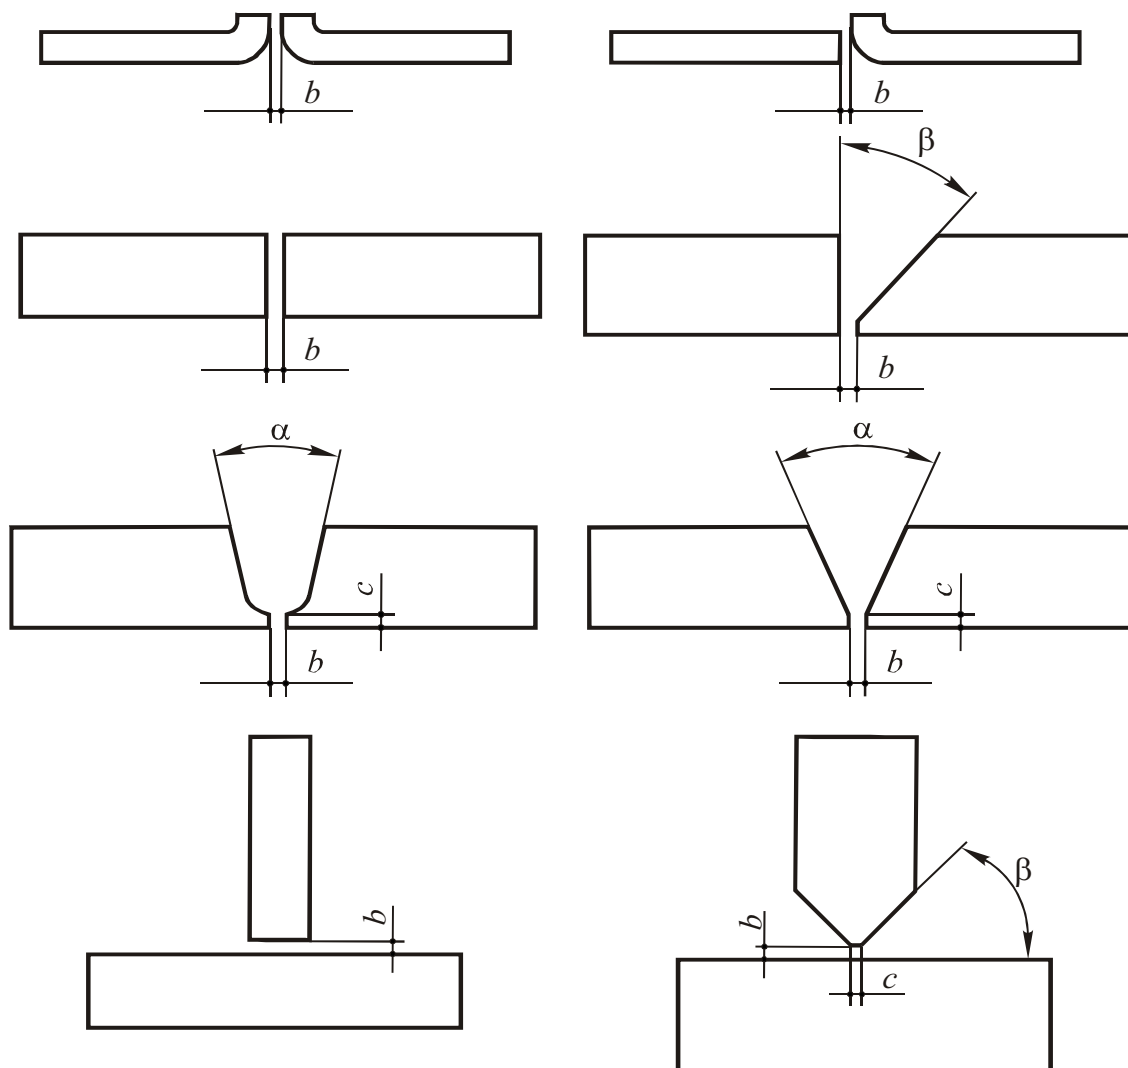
Конструктивные элементы подготовки свариваемых кромок
